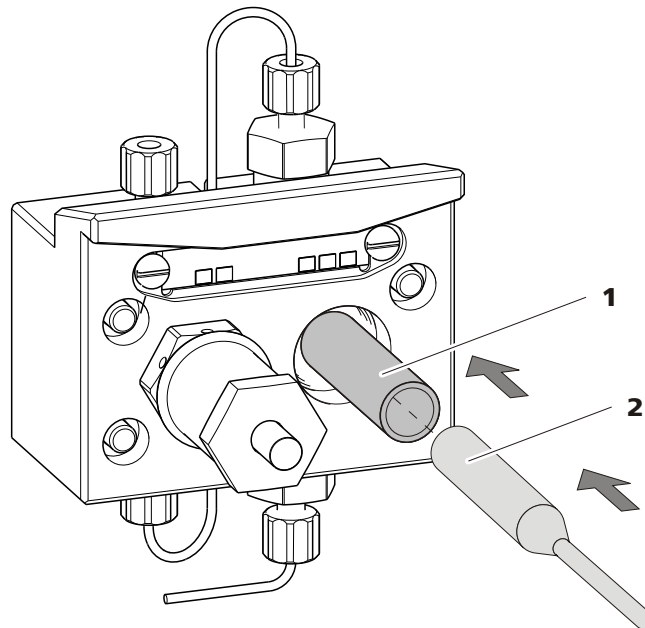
Kolbendichtung in Pumpenkopf einsetzen
